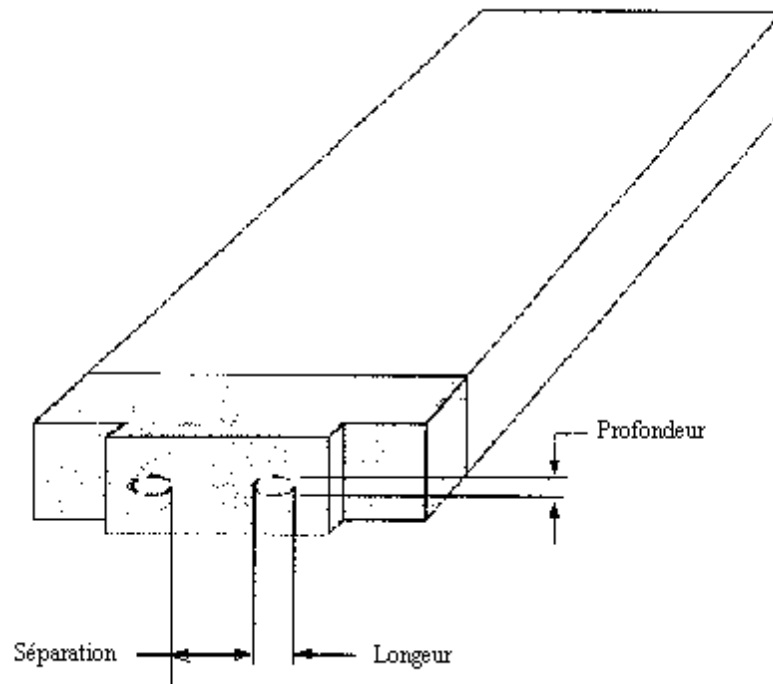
Dimensionnement des imperfections dans les surfaces apparentes de Soudures
